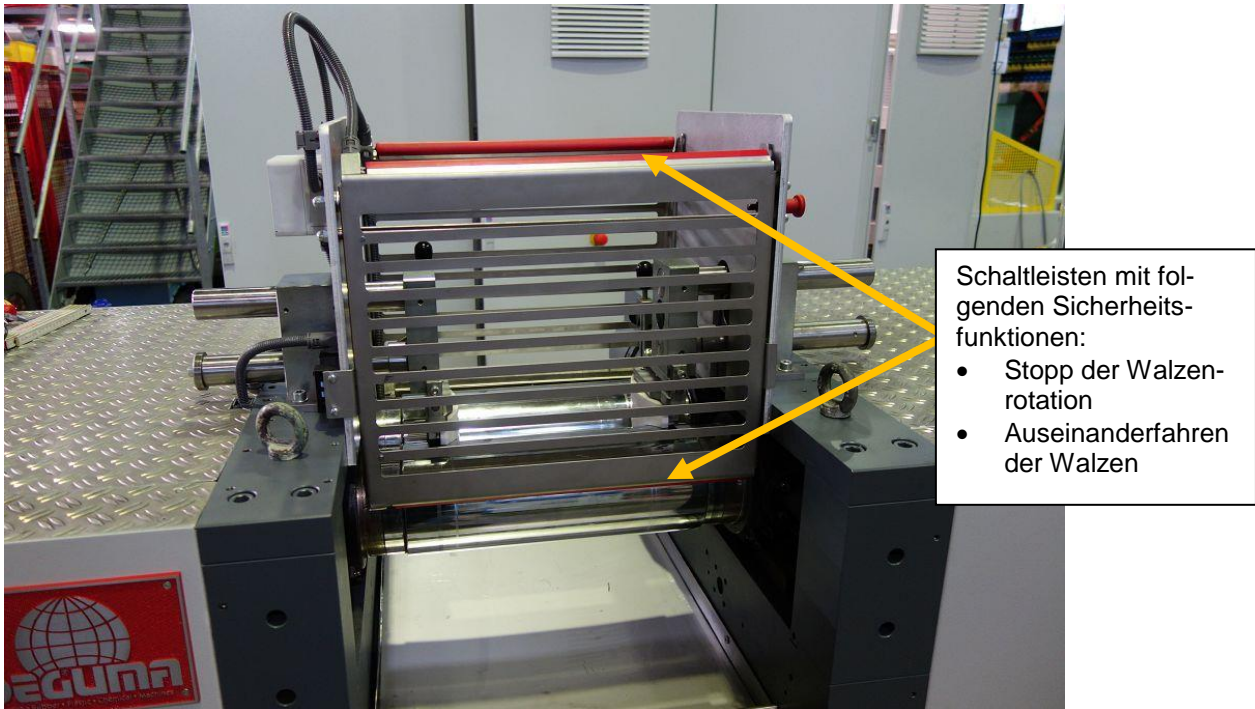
Walzwerk mit Walzendurchmesser D = 150 mm. Walzeneinzugspalt ist gesichert durch trennende Schutzeinrichtungen in Kombination mit Schutzeinrichtungen, die auf Berührung reagieren (Schaltleisten)
